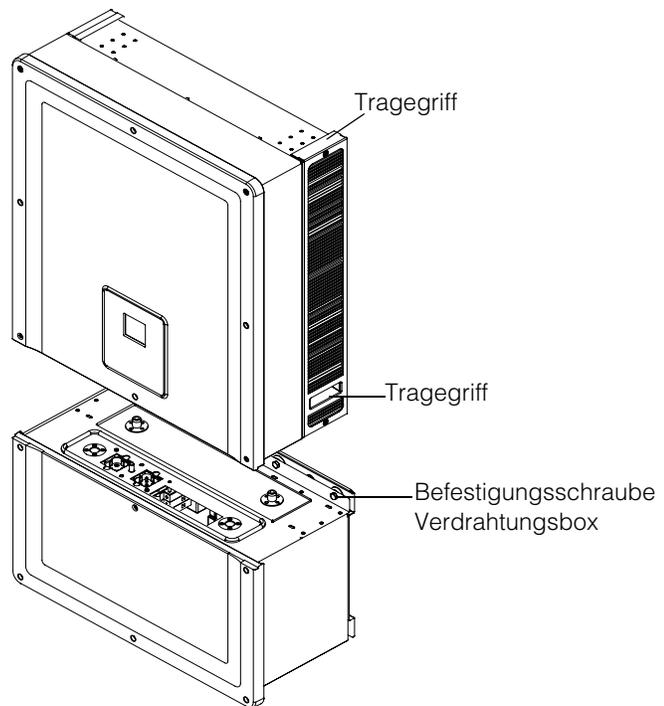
Wechselrichter und Verdrahtungsbox - Explosionszeichnung
